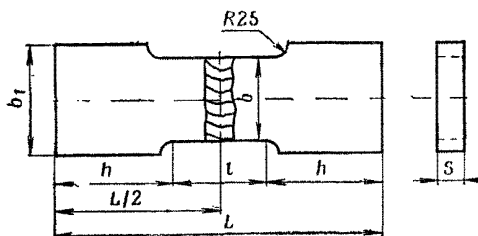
Форма и размеры плоского образца (разновидность), подготовленного для испытания сварного шва на разрыв
